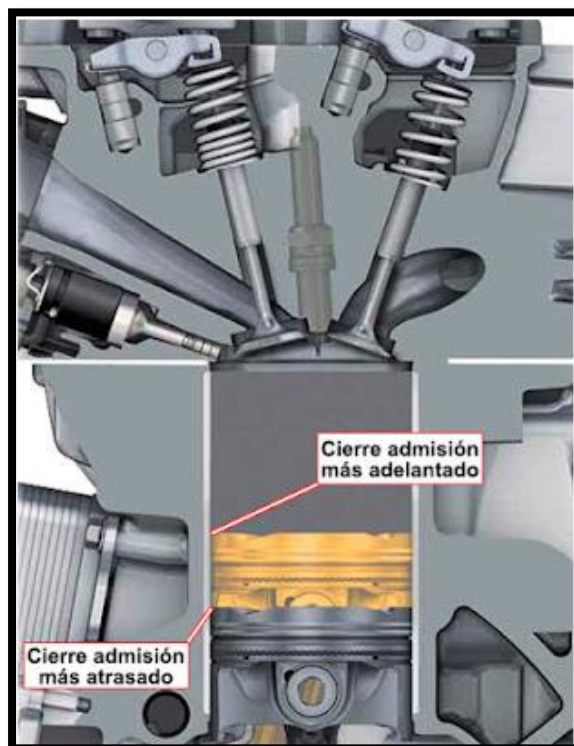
Cierre adelantado de la válvula de un motor ciclo Miller [66]
